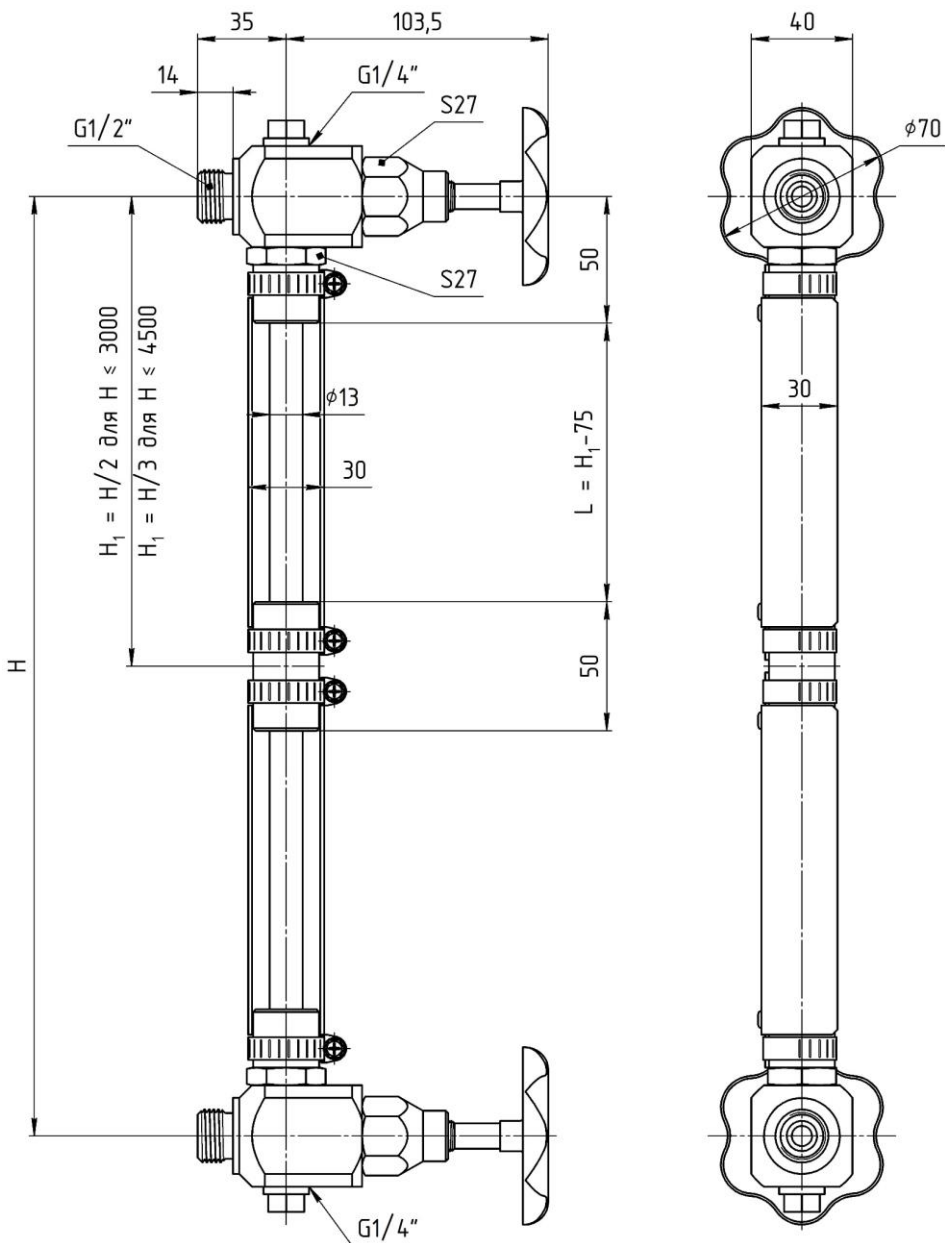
Общий вид указателя с присоединительной длиной  $H > 1500$  мм и резьбовым присоединением G1/2"
